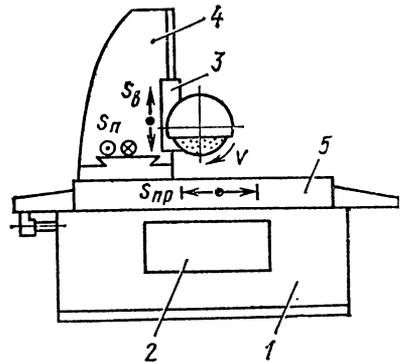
Общий вид плоскошлифовального станка с прямоугольным столом:
